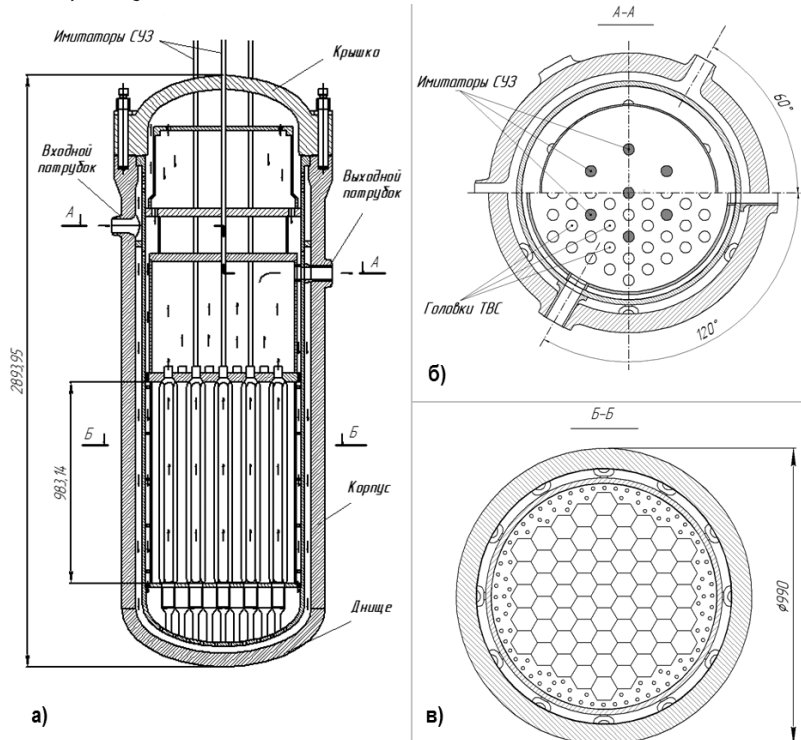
Общий вид конструкции гидравлической модели с одноходовой схемой движения
